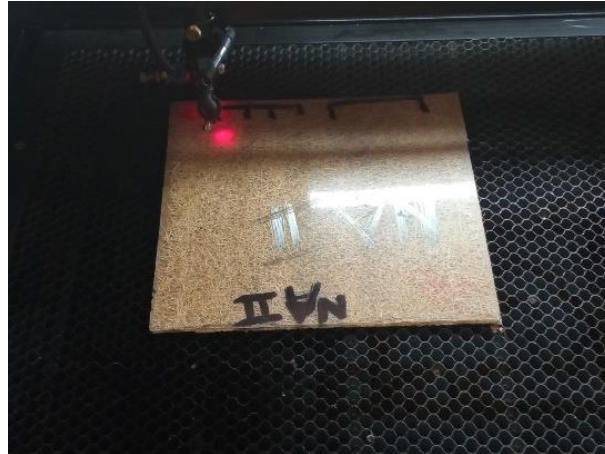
Découpage des éprouvettes de type haltère sur la plaque de NaOH de 2 plis
